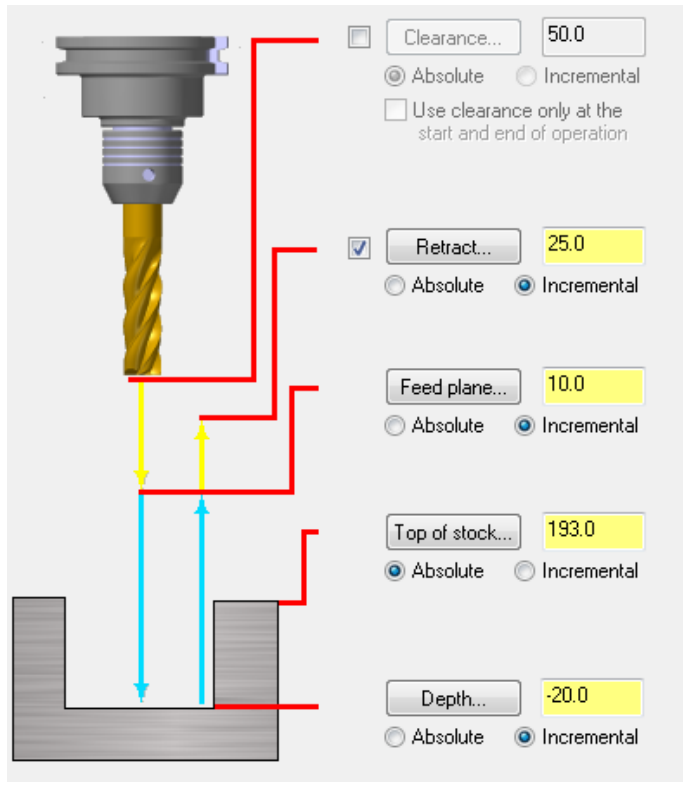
Parametry řezu pro čelní frézování kapes (*Pocket Facing*)
